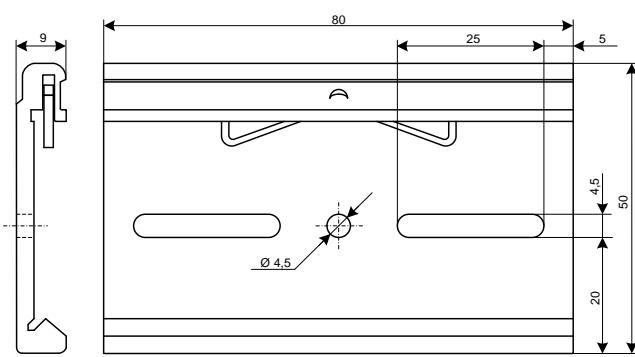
Приспособление для крепления модуля на монтажной рейке
